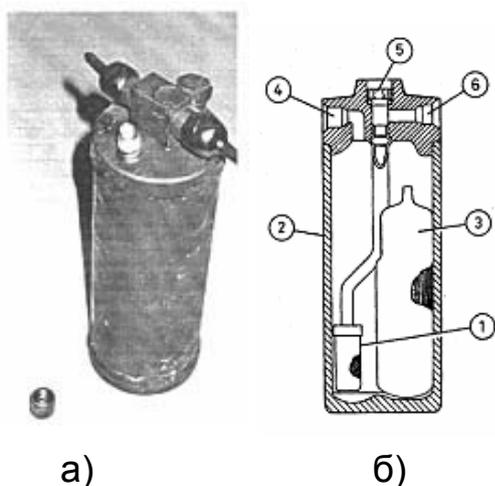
Внешний вид (а) и разрез (б) ресивера-осушителя:
